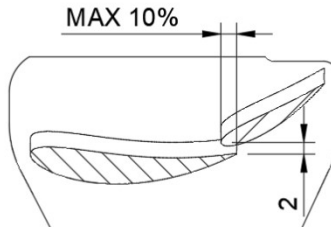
Overlap e slot alettone posteriore, R14.8.4 e R14.8.5
